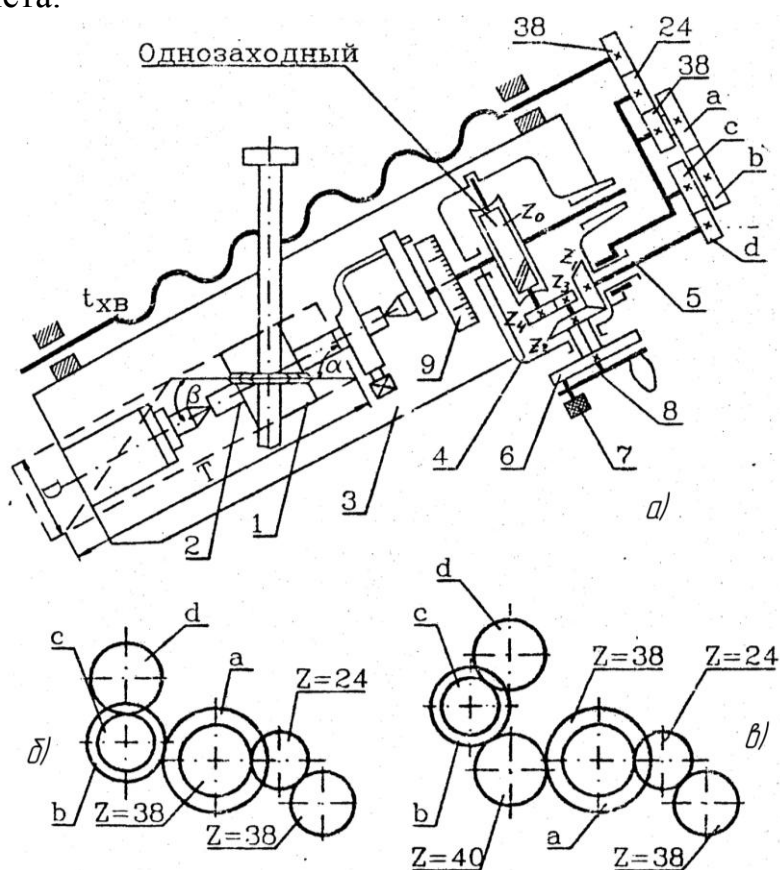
Схемы: *a* — наладки фрезерного станка на получение спиральных поверхностей; *б, в* — расположения сменных зубчатых колес с учетом направления фрезеруемых винтовых канавок,
